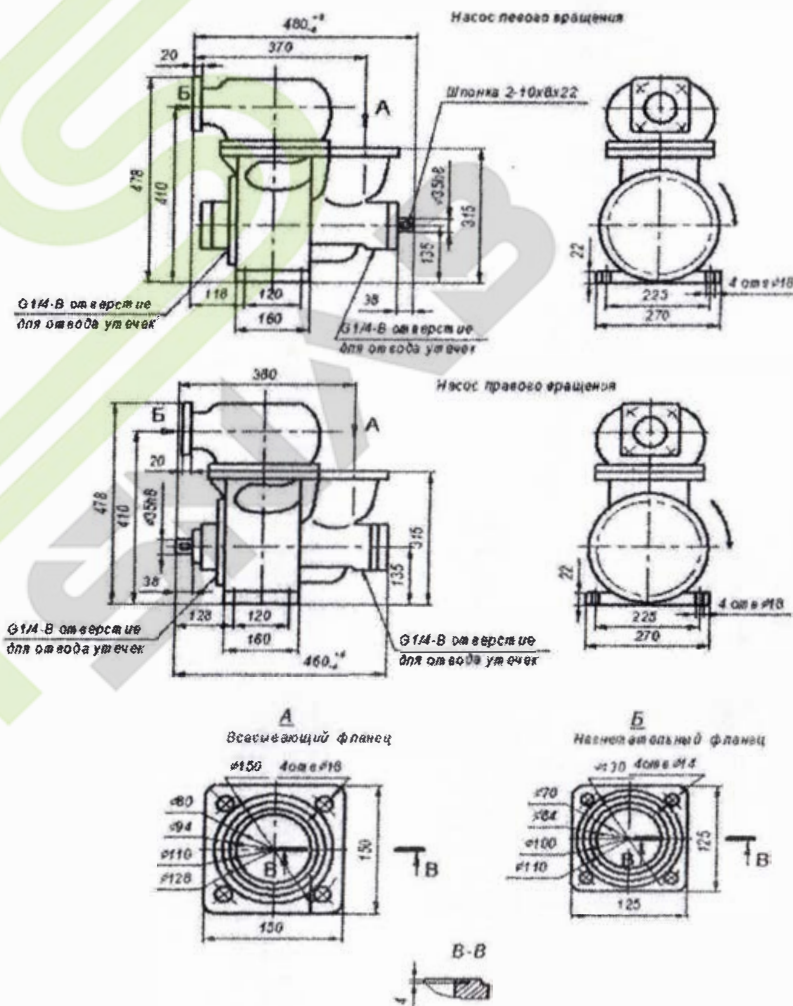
Габаритные и присоединительные размеры агрегатов электронасосных типа «1СЦП»
